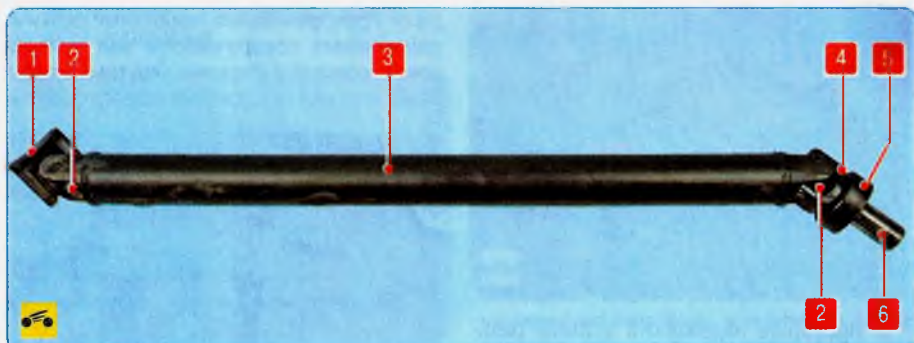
Задняя карданная передача автомобиля с задним приводом: 1 – задняя вилка; 2 – крестовина карданного шарнира; 3 – труба вала; 4 – передняя вилка; 5 – грязеотражатель; 6 – скользящий шлицевый наконечник
